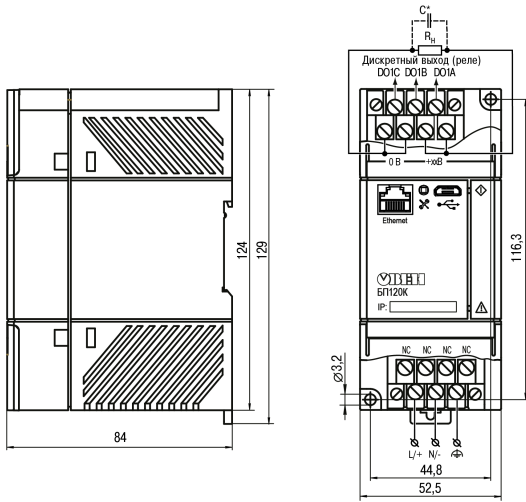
Габаритные, установочные размеры и подключение прибора
